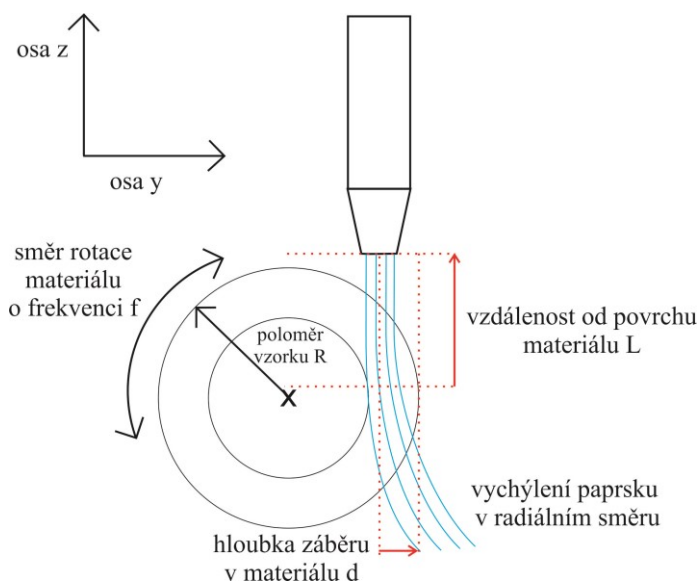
Schéma soustružení abrazivním vodním paprskem
